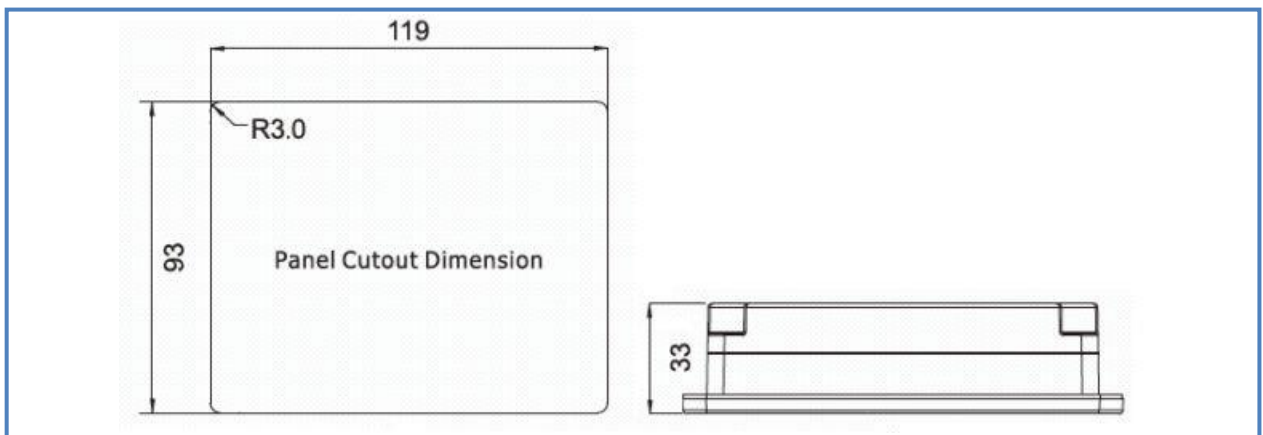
Abmessungen der Aussparung für die Montage der GRC
